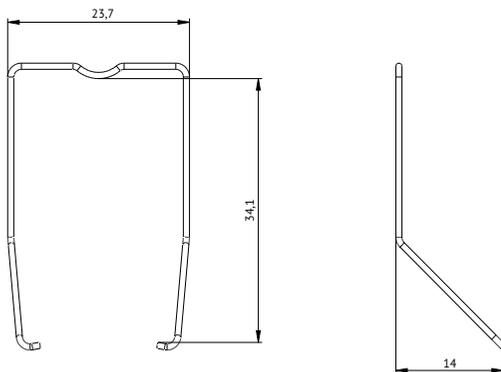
Габаритные, установочные присоединительные размеры фиксатора реле OptiRel 55-H5
